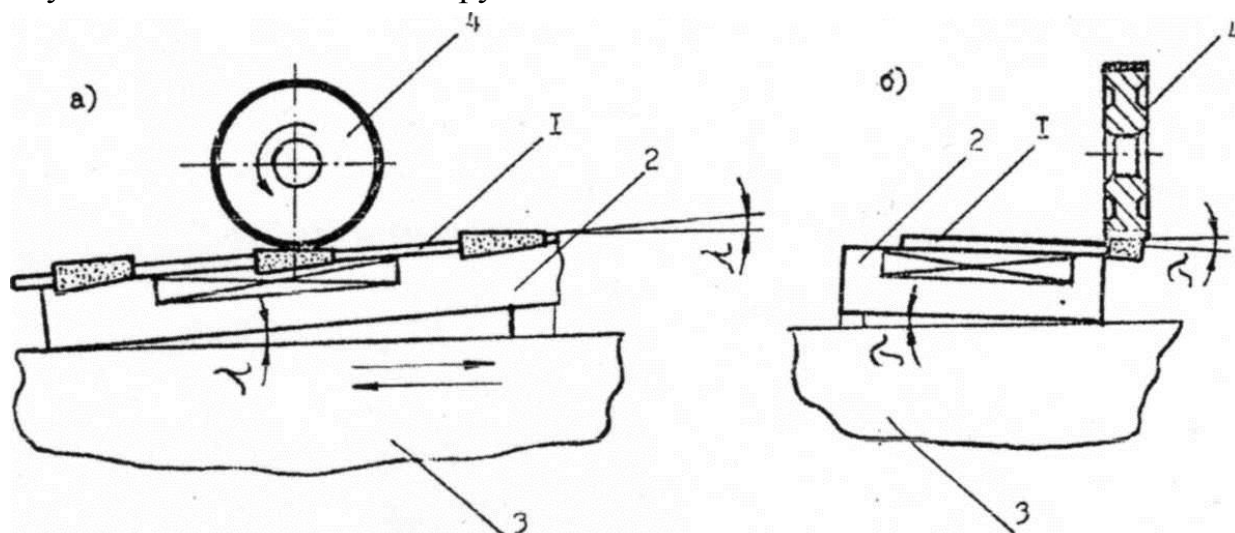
Схемы продольного (а) и поперечного (б) поднутрения зубьев ленточной пилы: 1 – ленточная пила; 2 – магнитная плита; 3 – стол заточного станка; 4- алмазный круг
